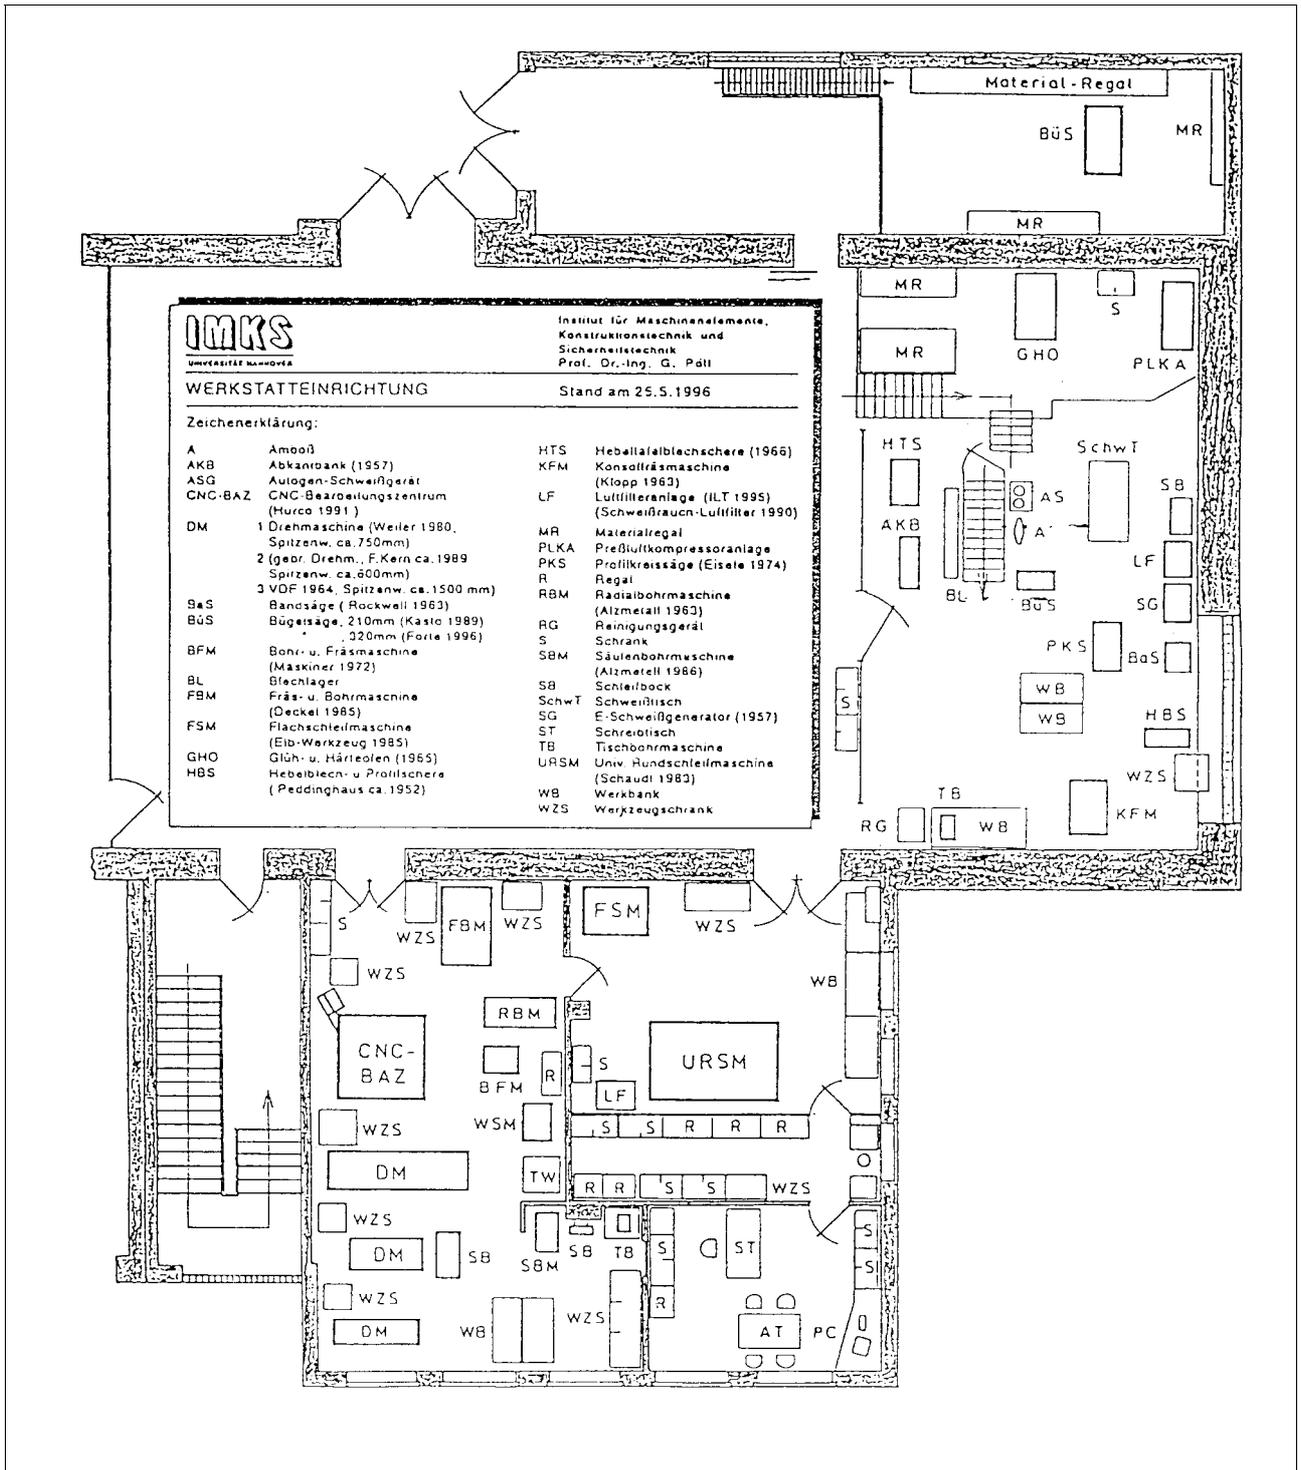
Werkstattgrundriß und Ausstattung IMKS Hannover
